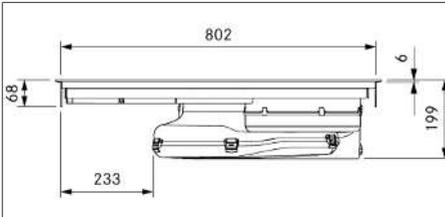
PUXU2/R dimensioni apparecchio vista frontale
